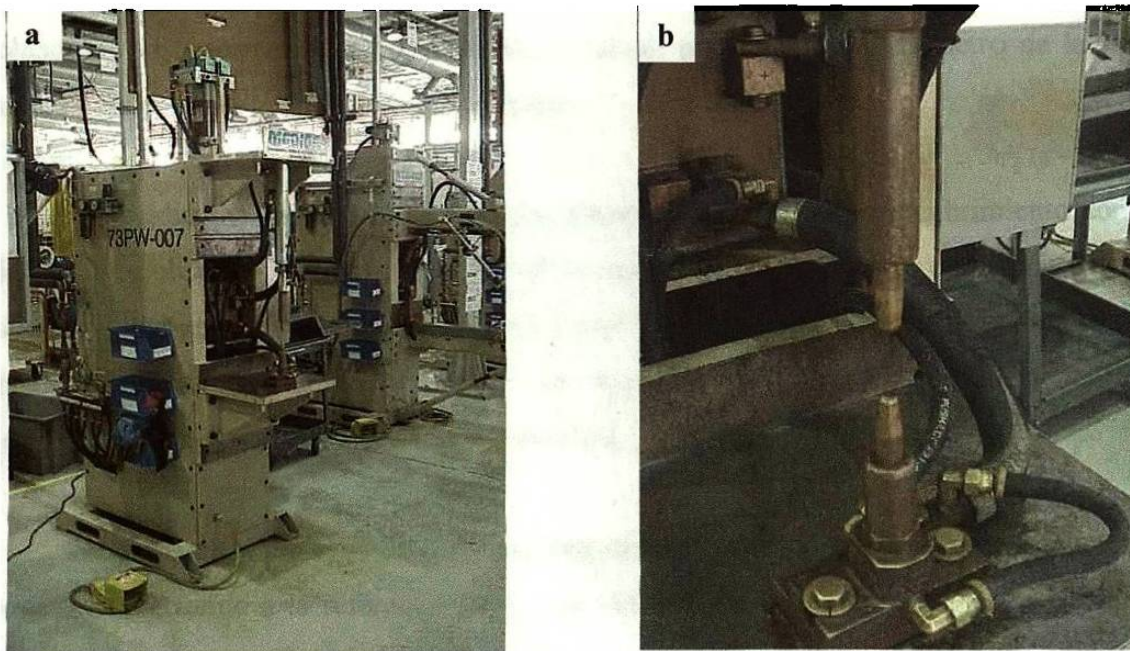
a) Muestra la máquina tipo pedestal en donde se realizaron las soldaduras, b) Muestra los electrodos superior e inferior de la máquina.
